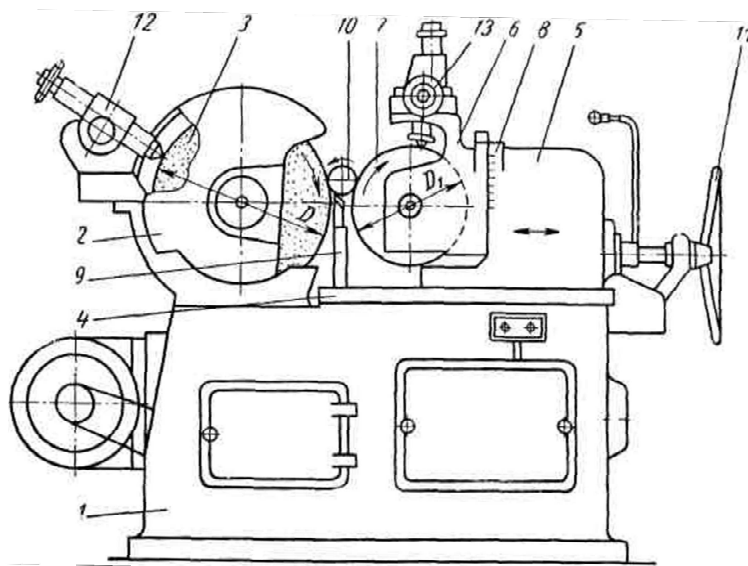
Компоновка бесцентрово-шлифовального станка
